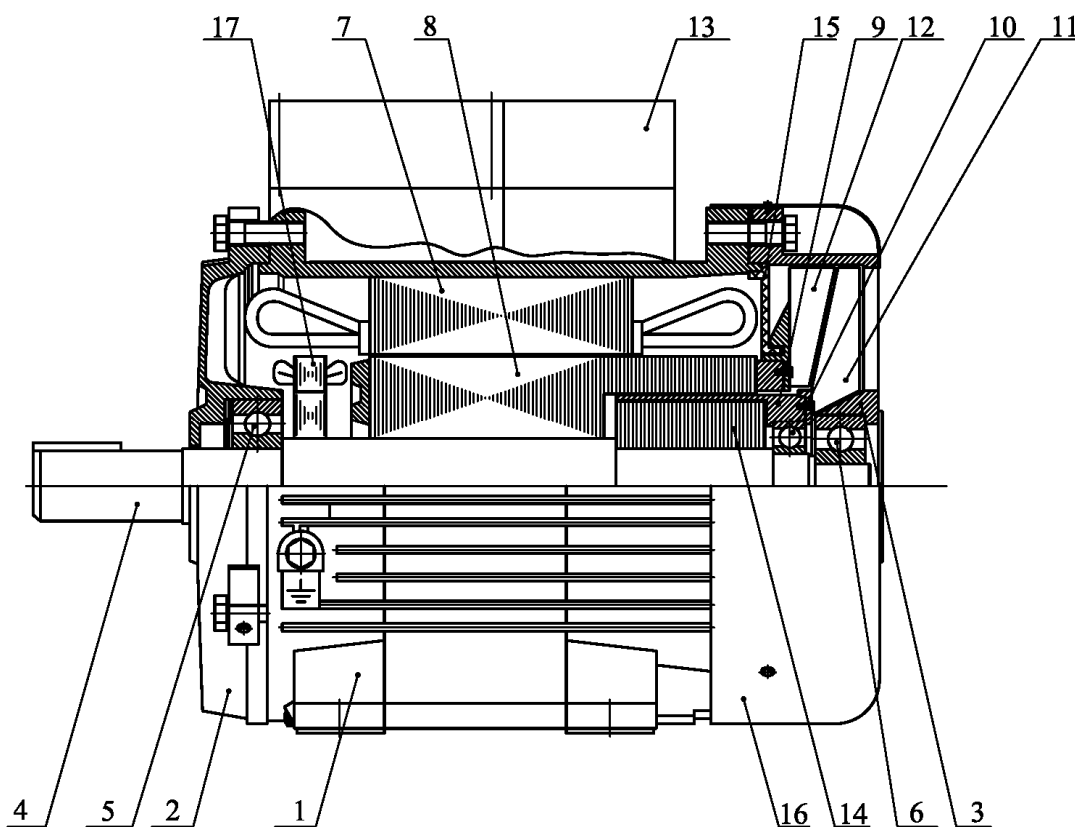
Особенности конструкции асинхронного электродвигателя по конструктивной схеме ДАС с двухроторной электромеханикой (ДАС – 12): 1 – станина электродвигателя; 2, 3 – подшипниковые щиты; 4 – вал силового ротора; 5, 6 – подшипники силового ротора; 7 – магнитопровод статора с обмоткой; 8 – удлиненный магнитопровод силового ротора со стержневой обмоткой; 9 – малый ротор вентилятора; 10 – подшипник малого ротора вентилятора; 11 – вентилятор, закрепленный на малом роторе; 12 – лопасти теплорассеивателя вентилятора силового ротора; 13 – клеммная коробка со встроенным электронным блоком регулирования; 14 – магнитопровод малого ротора вентилятора; 15 – кольцевая перегородка; 16 – кожух; 17 – датчик скорости
